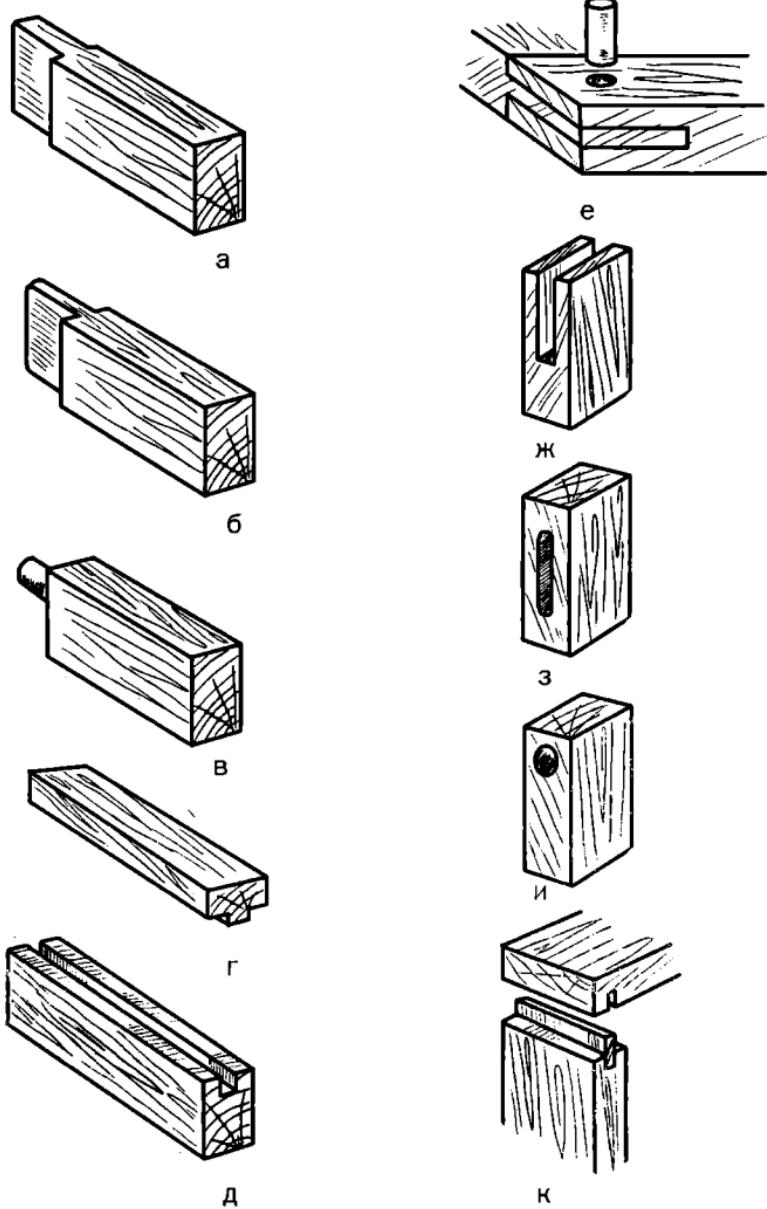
Основные элементы шиповых соединений: а, б — плоские шипы; в — круглый шип; г — гребень; д — шпунт; е — шкант; ж — проушина; з — гнездо для плоского шипа; и — гнездо для круглого шипа; к — рейка
